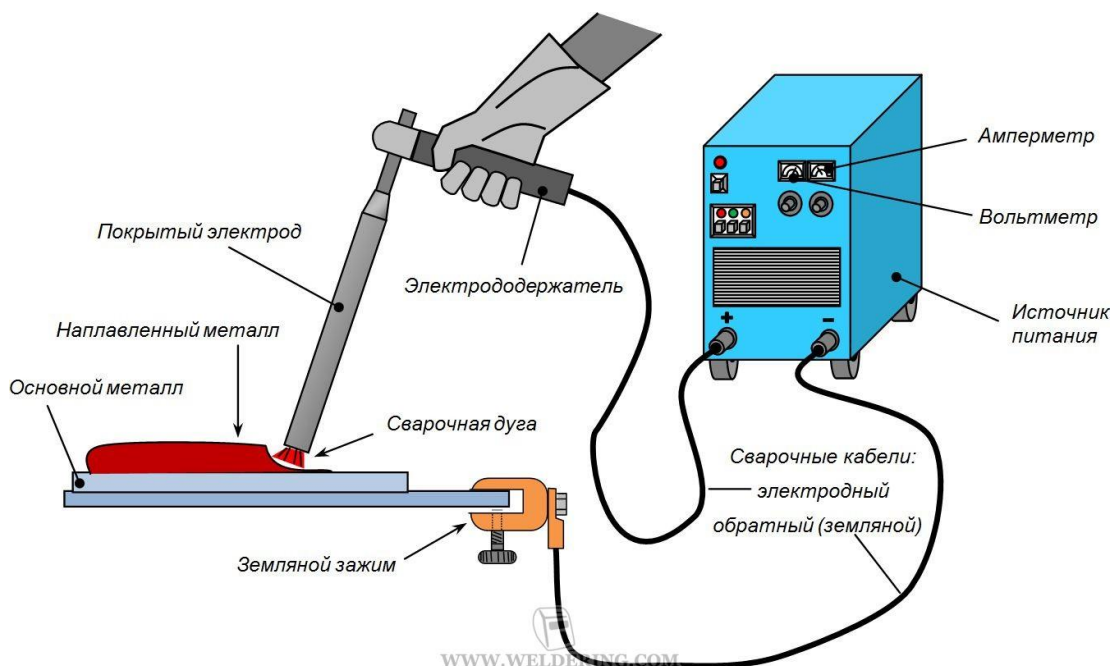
Дуговая сварка покрытыми электродами
